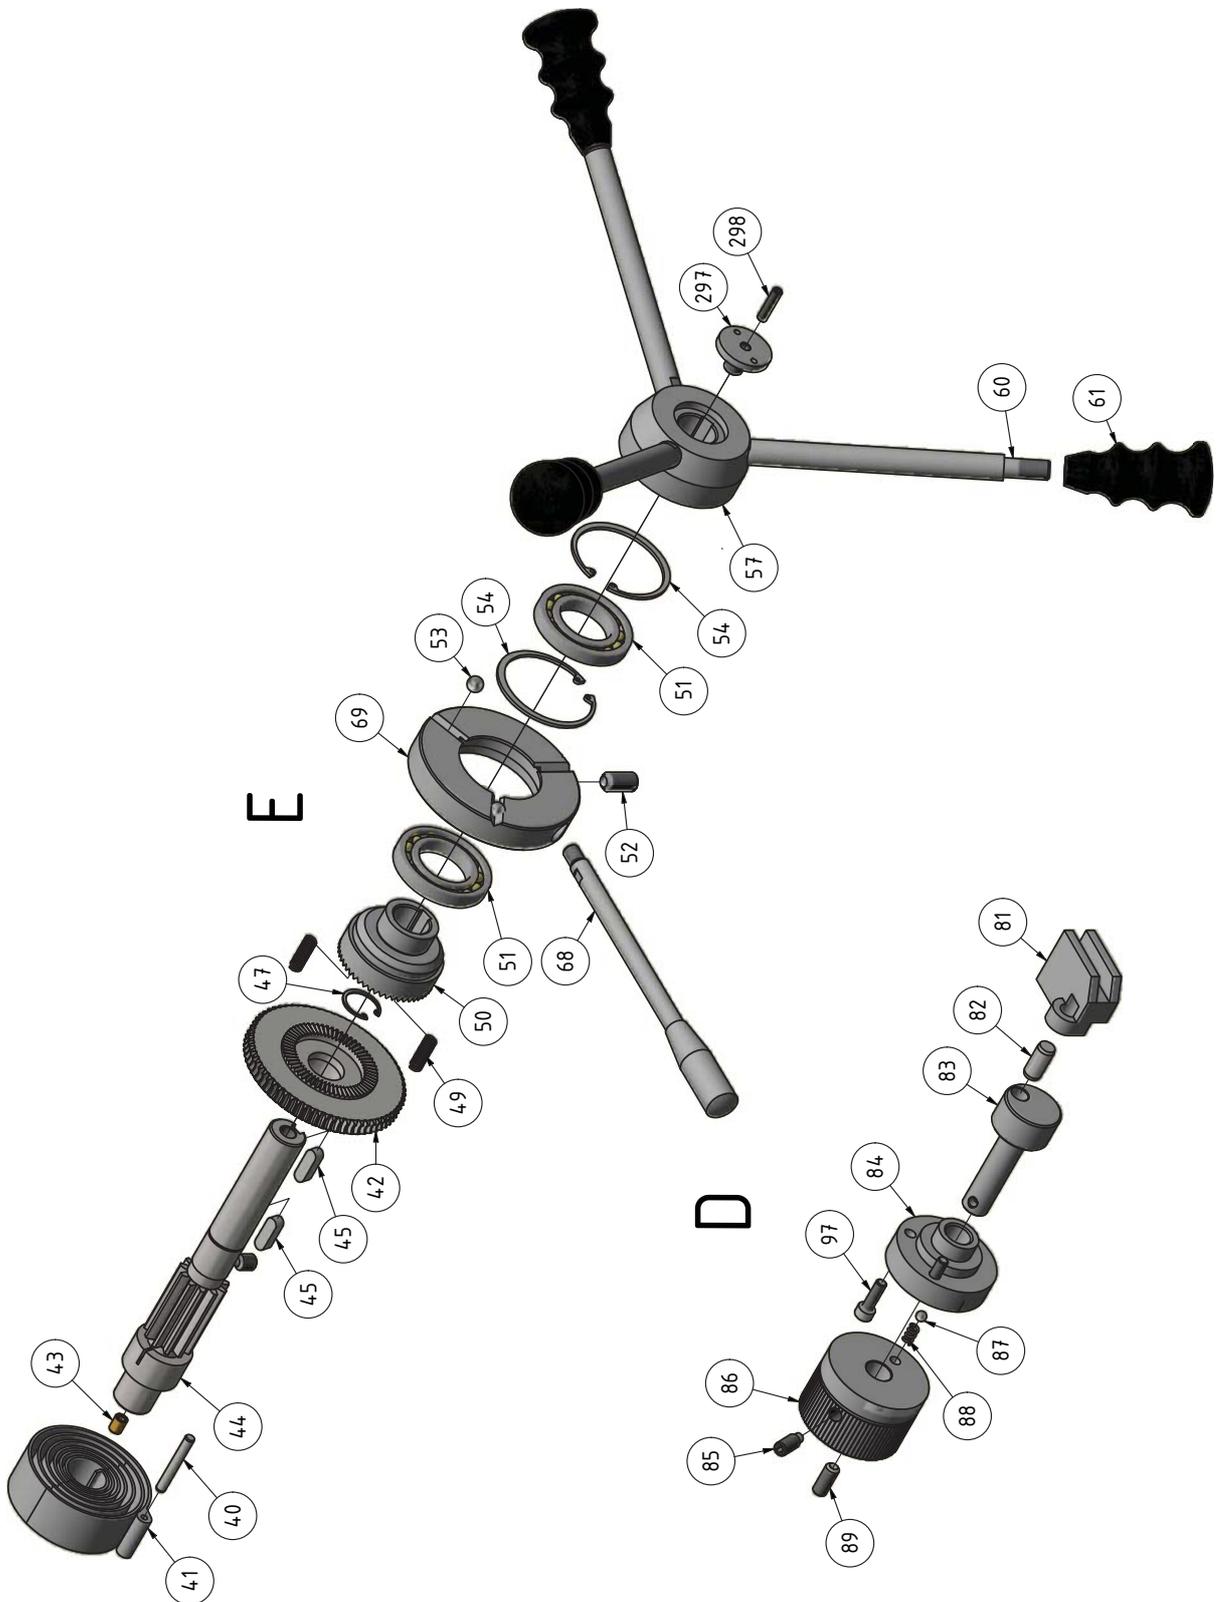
Vorschubgetriebe 2 von 4 - Feed gear box 2 of 4
